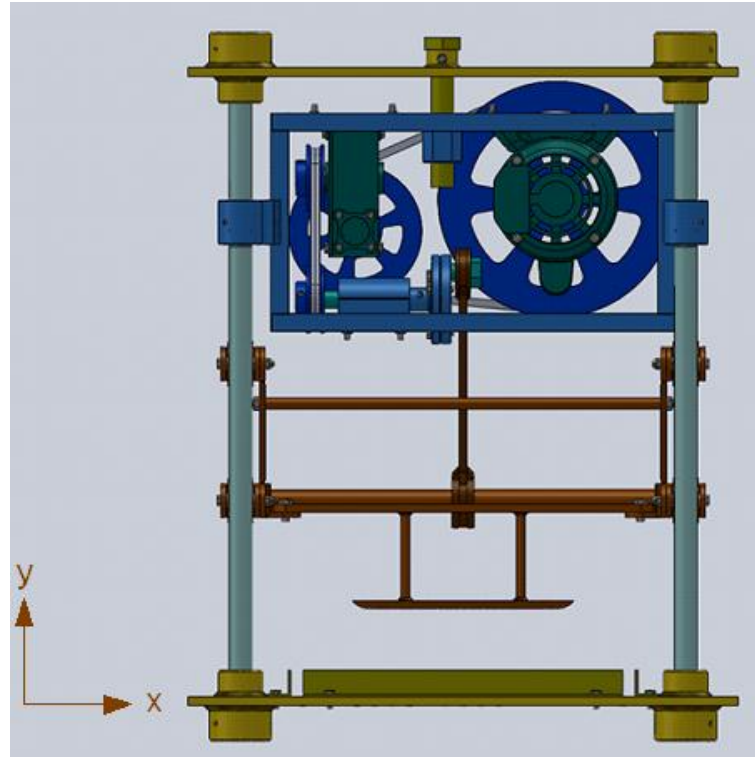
Equipo de ensayo ensamblado (vista frontal).
